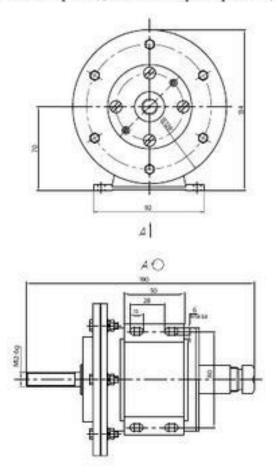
Габаритные и присоединительные размеры ПП МГДУ УП.
